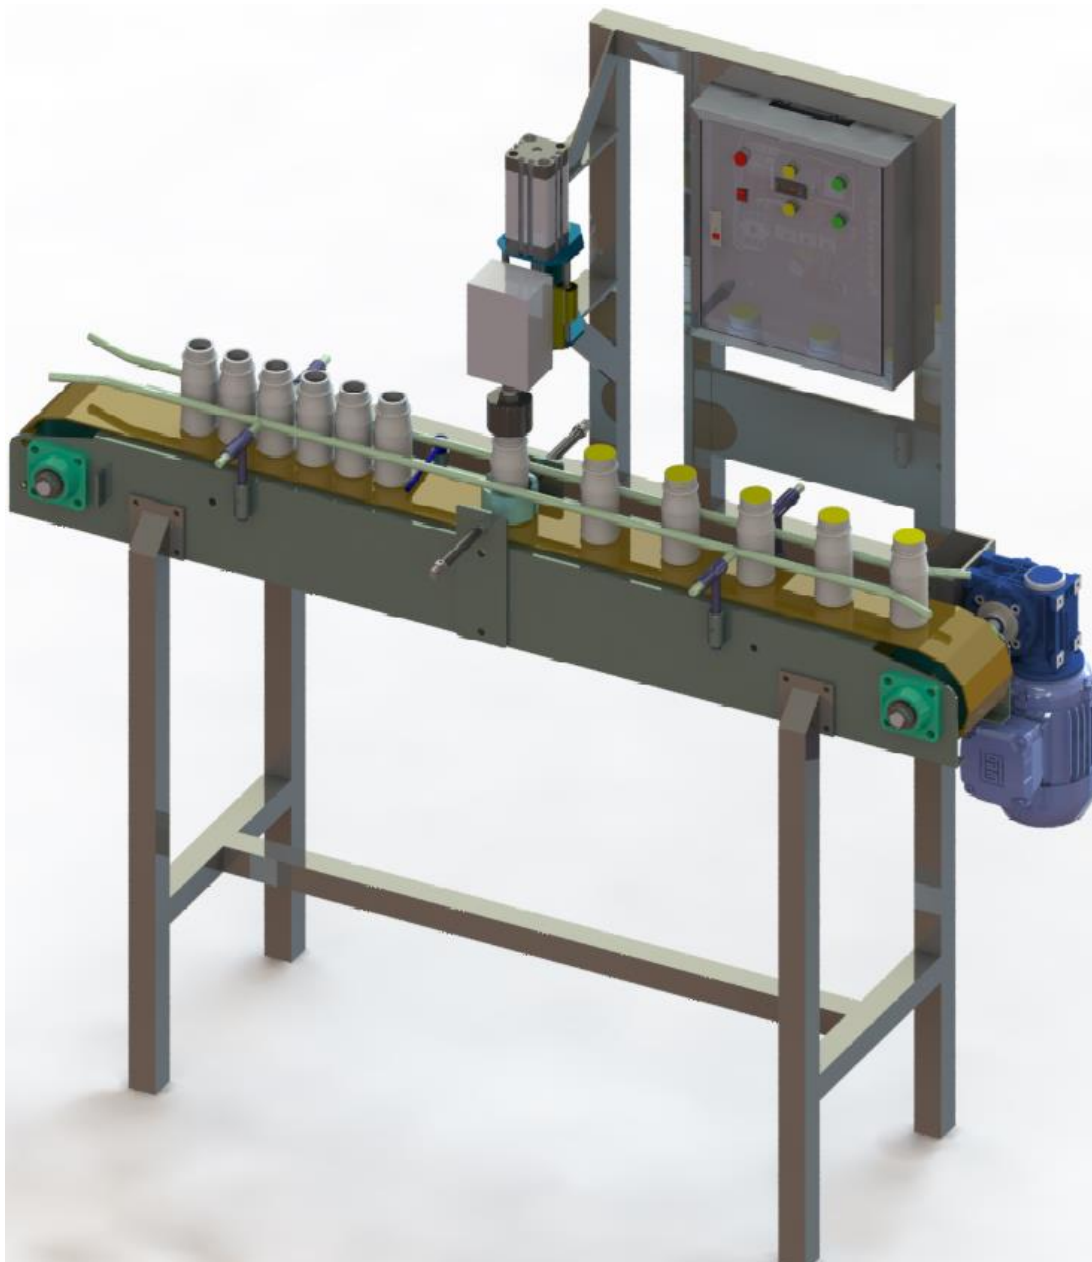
13 Ensamblaje completo de la máquina tapadora
